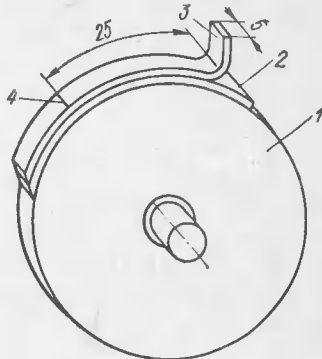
Схема образца для измерения прочности сцепления: 1 — ролик; 2 — основа; 3 — покрытие; 4 — надрез
